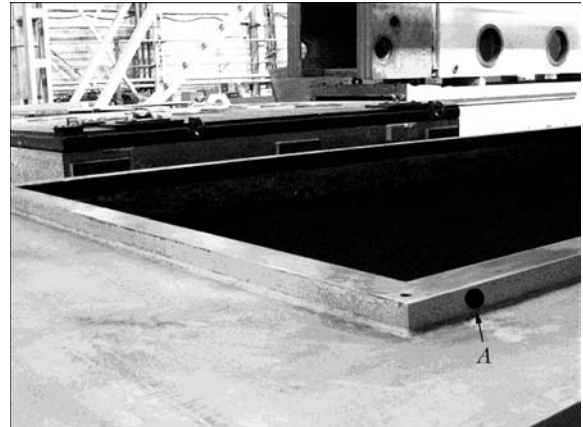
Конструкция фланца камеры подачи шихты для контроля вакуумной плотности сварных швов; А — отверстие во фланце вакуумной камеры
